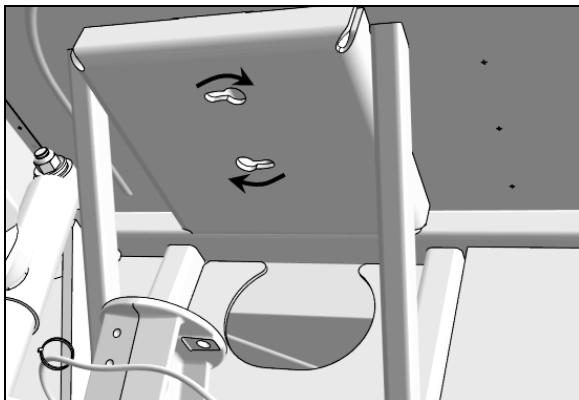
PLAQUE DE MONTAGE SUPÉRIEURE DU RESSORT PNEUMATIQUE
